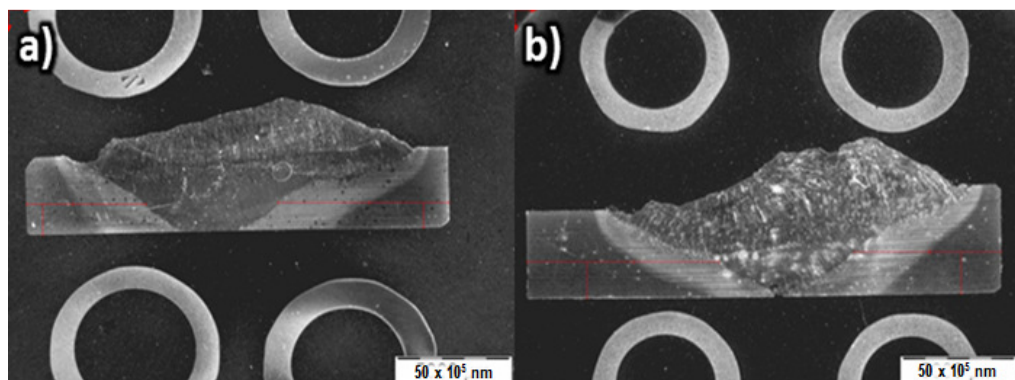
Corte transversal de la soldadura vista a 10X realizada a) 10m y b) 15m de profundidad.
